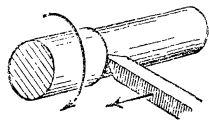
Вращательное движение детали на токарном станке и поступательное движение резца.
